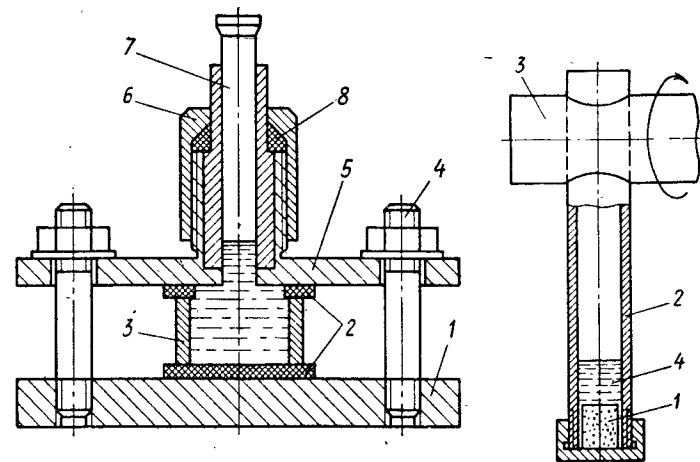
Приспособление для пропитки фторопластом втулок с внутренней рабочей поверхностью
